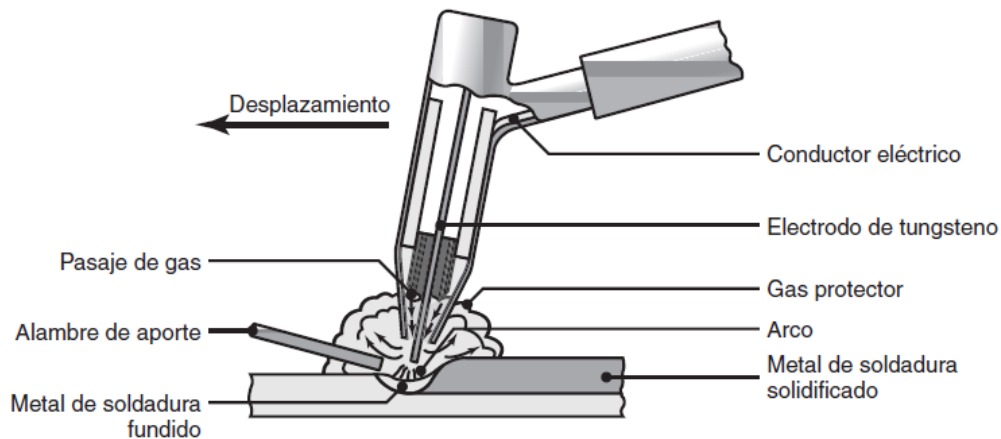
Dispositivo de soldadura TIG. [33]
